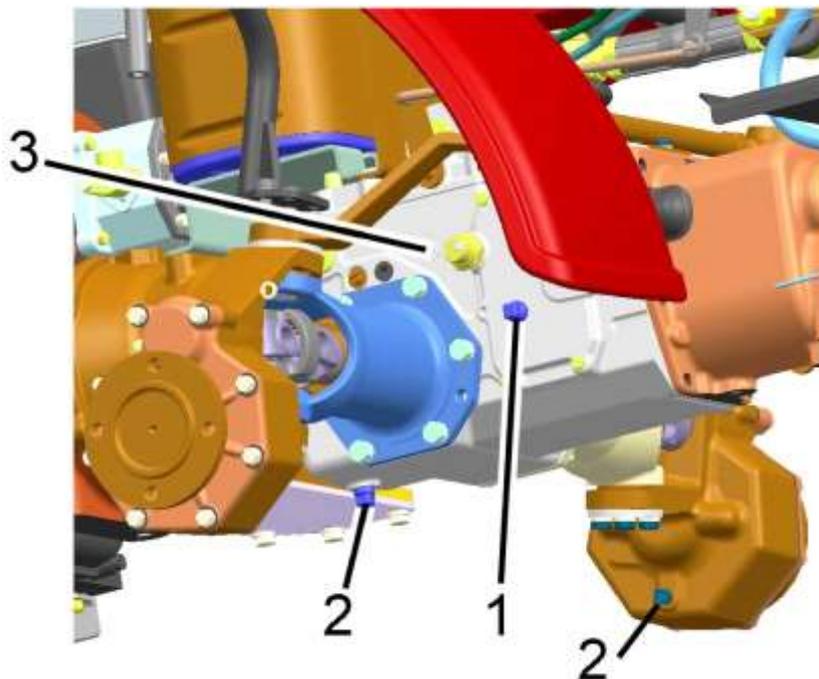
Проверка уровня масла в корпусе главной передачи ПВМ и КП
